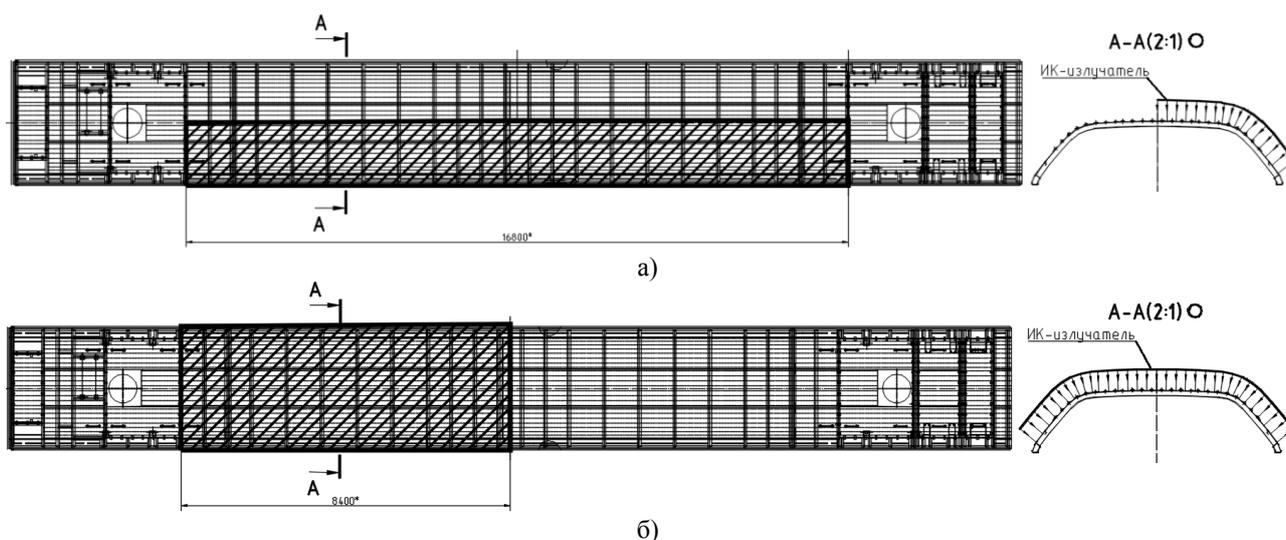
Минимальная охватываемая обогревателями поверхность крыши при расположении обогревателей: а – по схеме 1; б – по схеме 2
